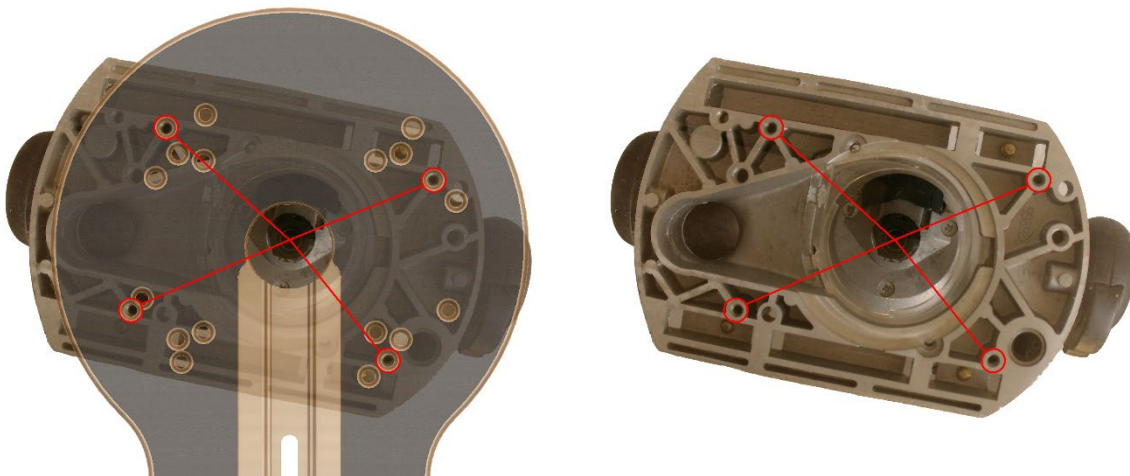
schema di foratura per DW625 - aspirazione sul lato destro
